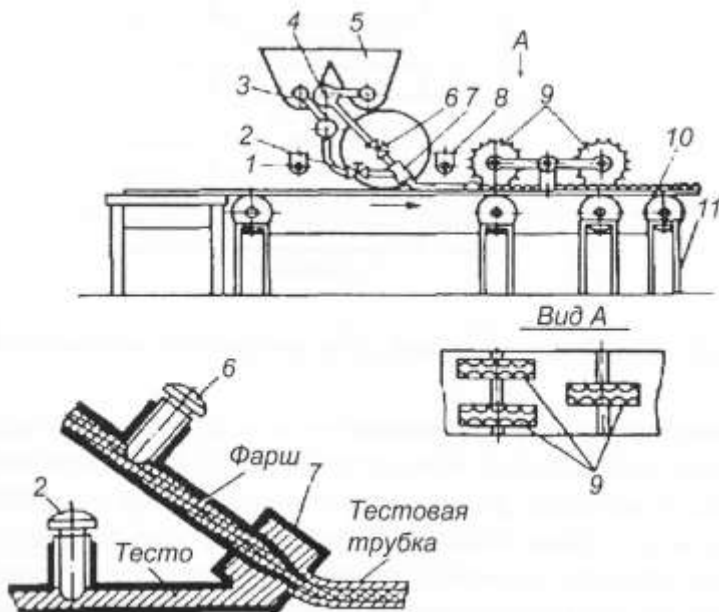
Схема пельменного автомата: 1 - бункер посыпки лотков; 2, 6 — регулировочные краны; 3 — бункер для теста; 4 — коллектор распределения фарша; 5 — бункер для фарша; 7 — формующая головка; 8 — бункер посыпания тестовых трубок; 9 — штампующие барабаны; 10 — ленточный конвейер; 11 — станина.
